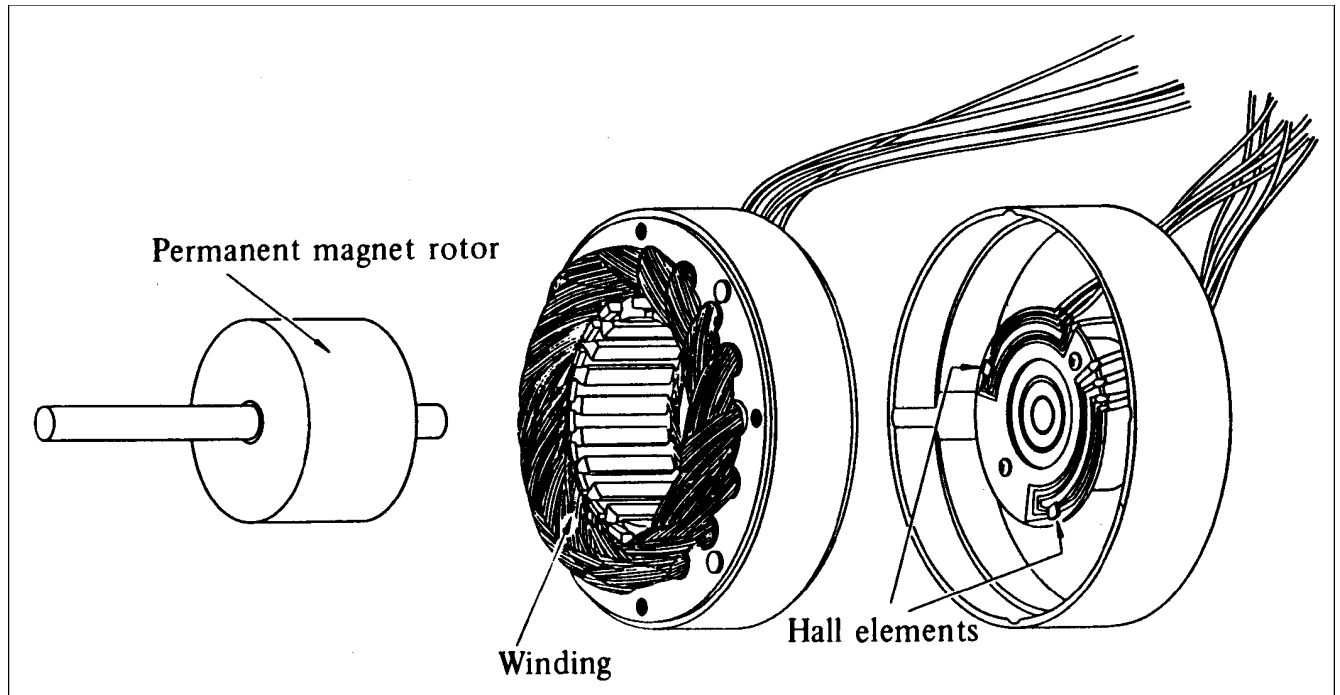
Motor Brushless desmontado (“da esquerda para direita” rotor, estator e sensor Hall).
